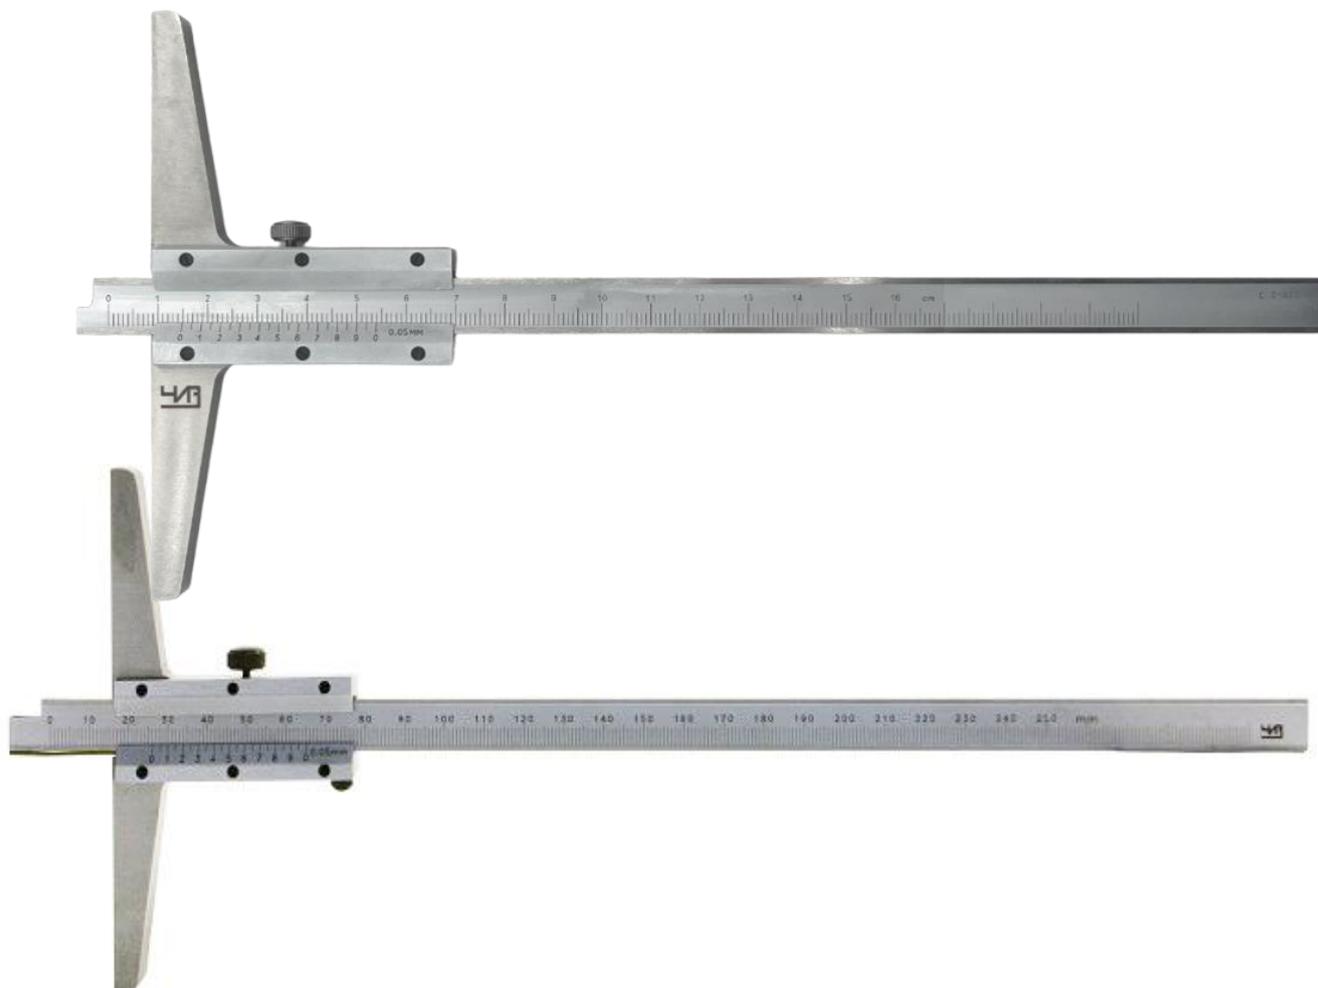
Общий вид штангенглубиномеров модификации ШГ со ступенчатым торцом штанги
